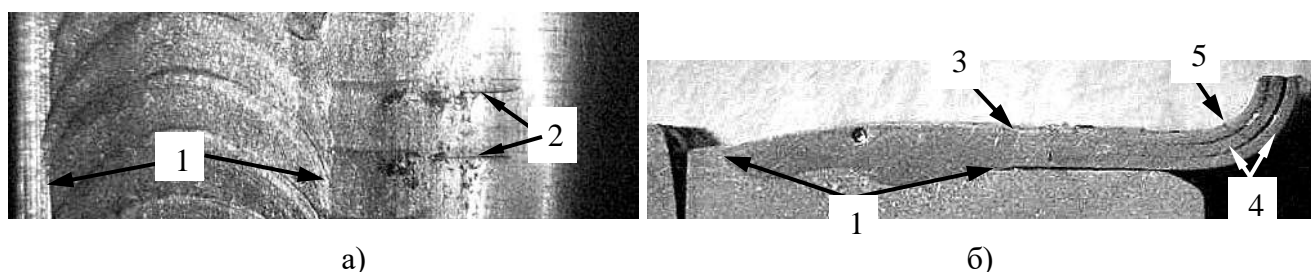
2 Макроизображения 2-х трещин на поверхности внешнего диаметра фланца 1 (а) и поперечного сечения сварного шва приварки слоёв сильфона к поверхности внешнего диаметра фланца 1 (б). Стрелками показаны: 1 – сварной шов, 2 – трещины, 3 - местоположение очагов зарождения трещин, 4 – слои сильфона, 5 – изгиб гофра. Увеличено.
